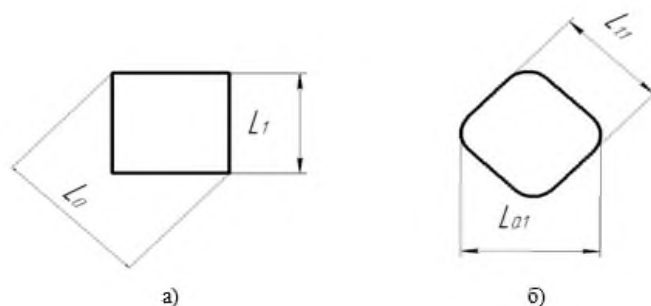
а) Исходные размеры заготовки кубической формы,
